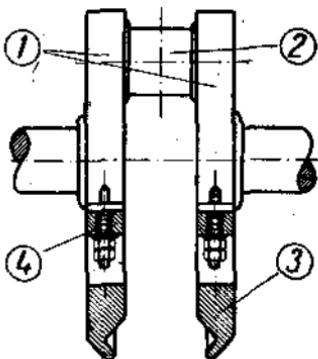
Коленчатый вал воздушного компрессора типа Бородино с противовесами.
